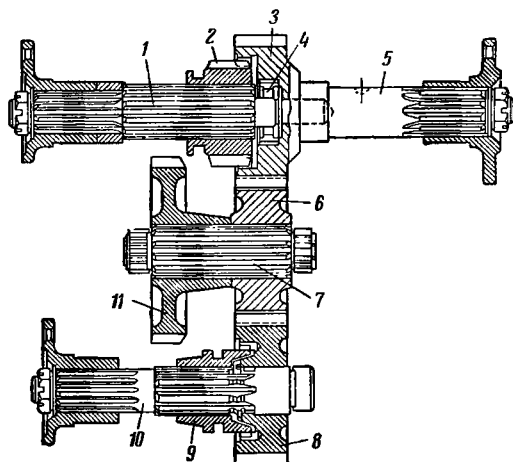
Схема раздаточной коробки автомобиля ГАЗ-63.
